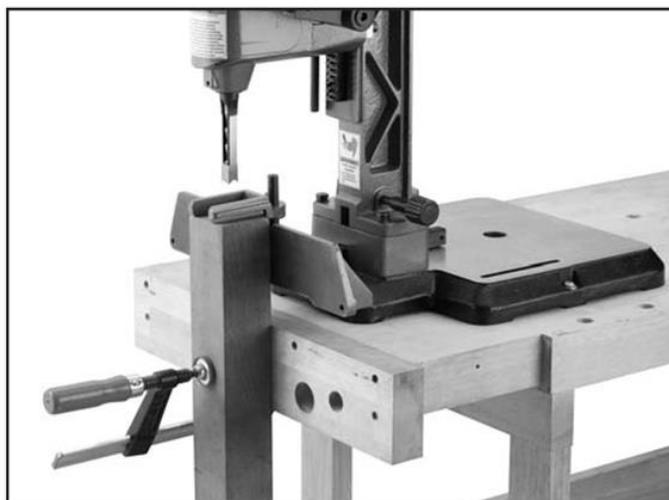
Стойка повернута на 180° для получения заготовки большего размера.
